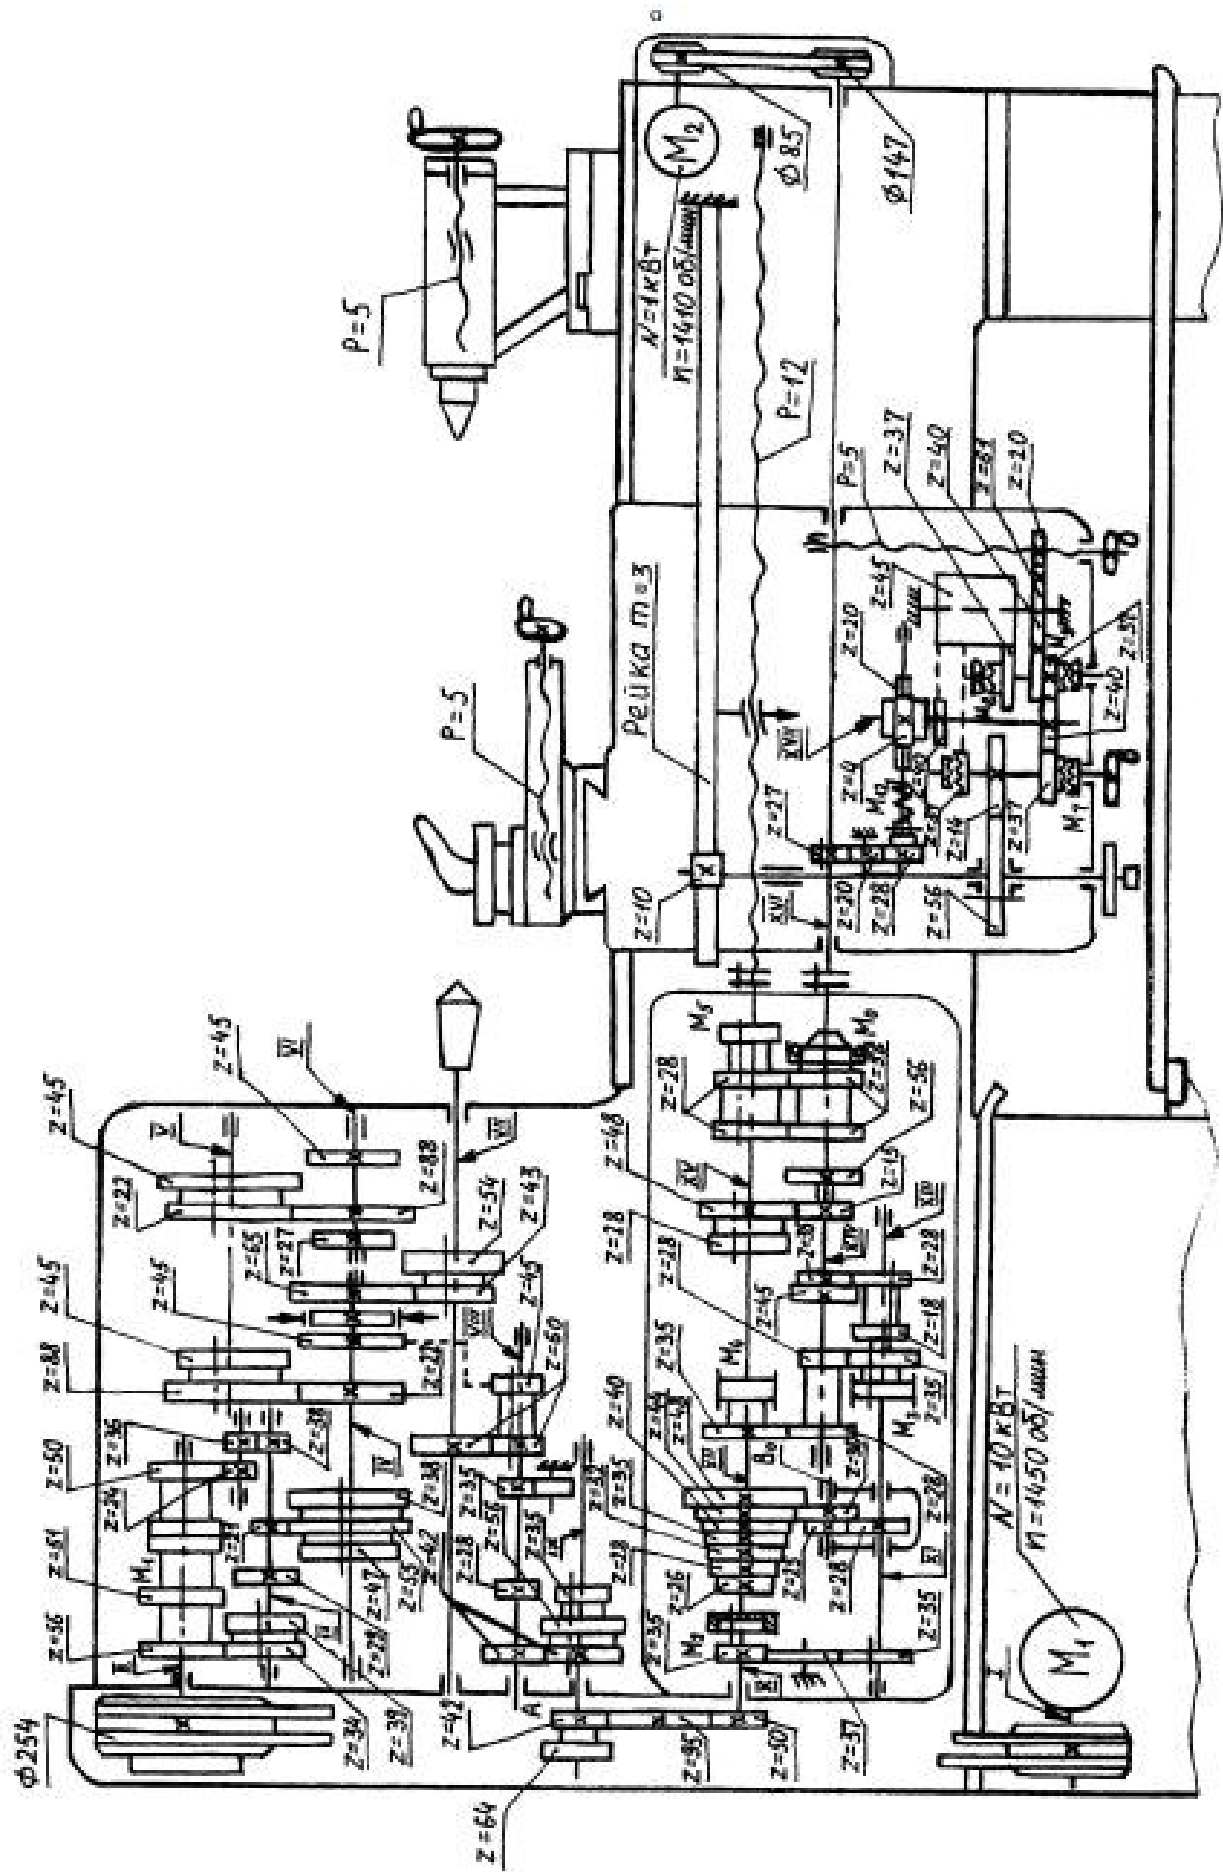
Кинематическая схема токарно-винторезного станка 1K625
